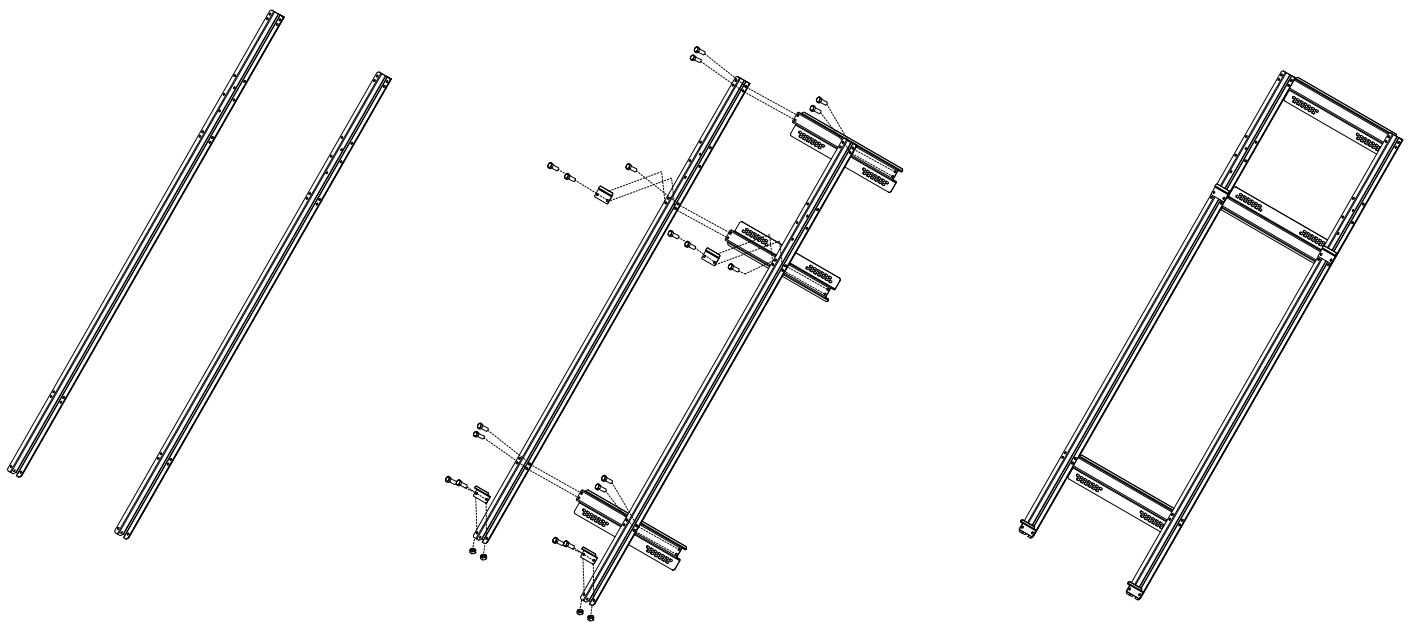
Dimensioni e ingombri staffaggio tetto inclinato
